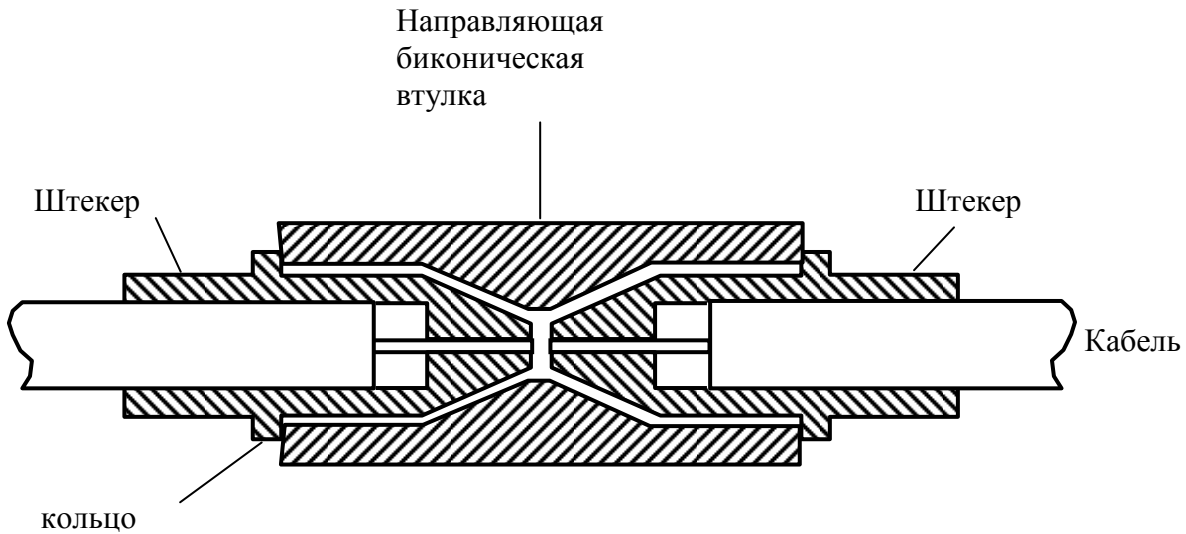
Разрез конструкции соединителя с конической втулкой
